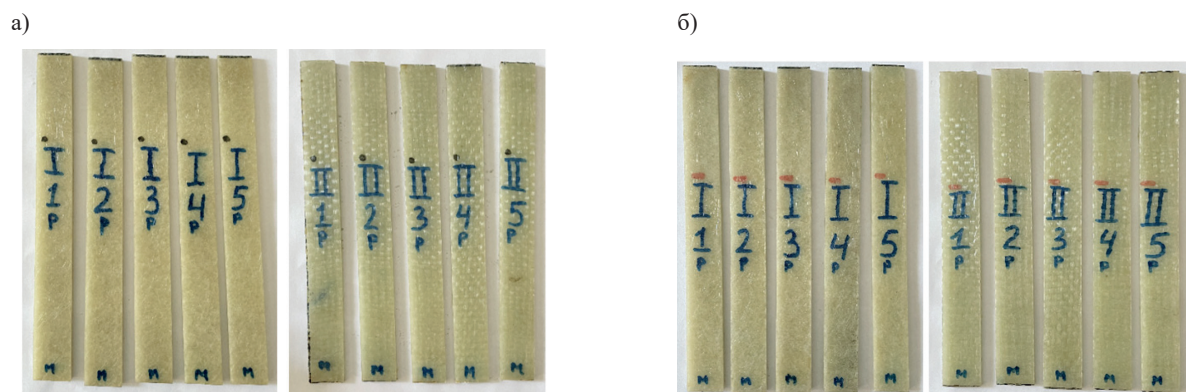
Образцы двух разных схем армирования для испытания на растяжение:
